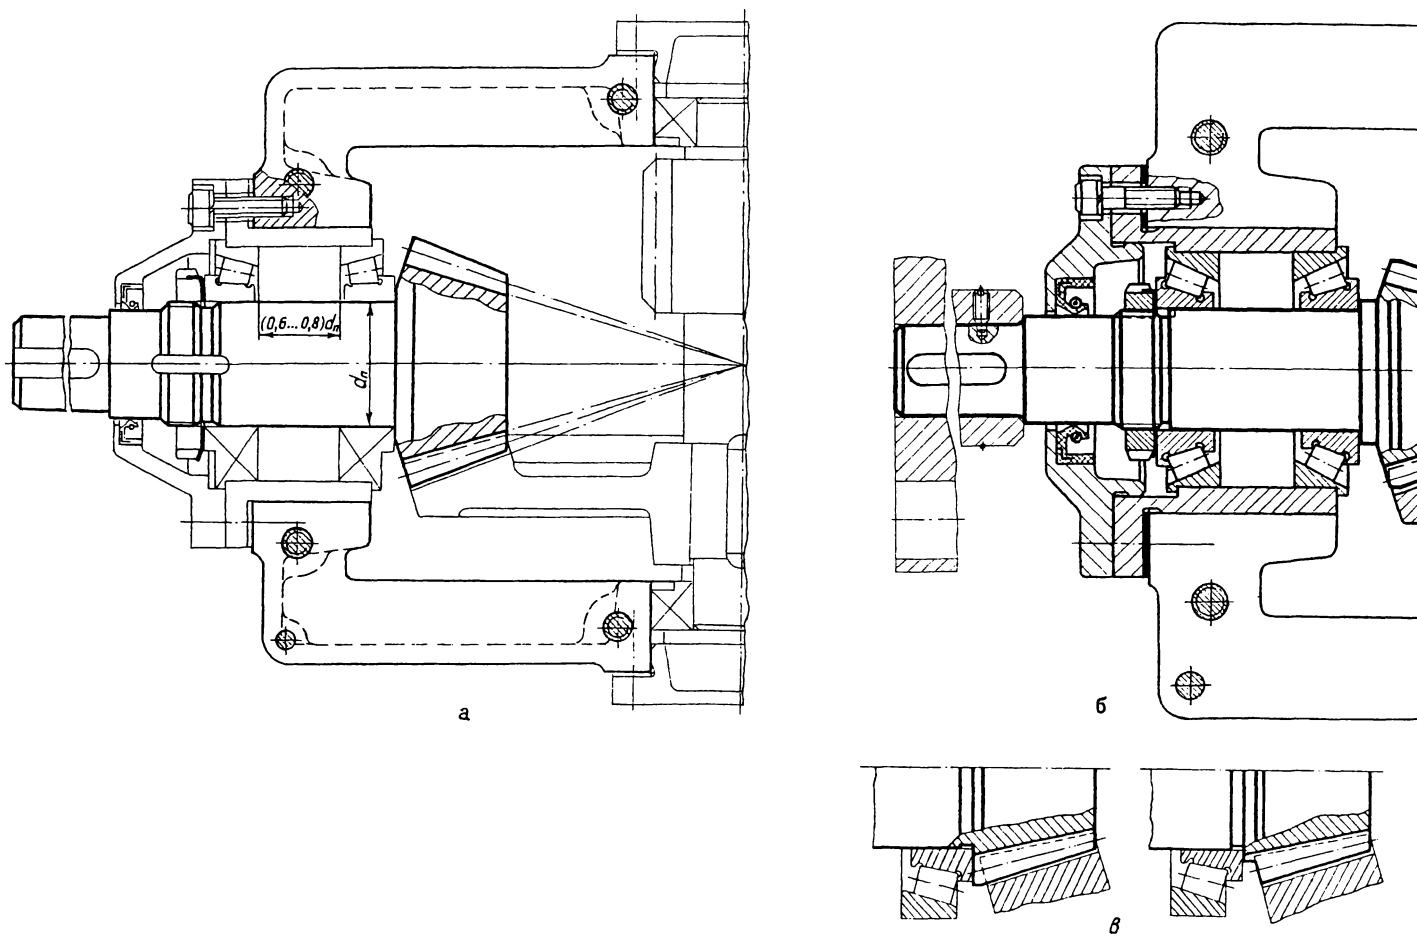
Вал-шестерня конической передачи коническо-цилиндрического зубчатого редуктора
